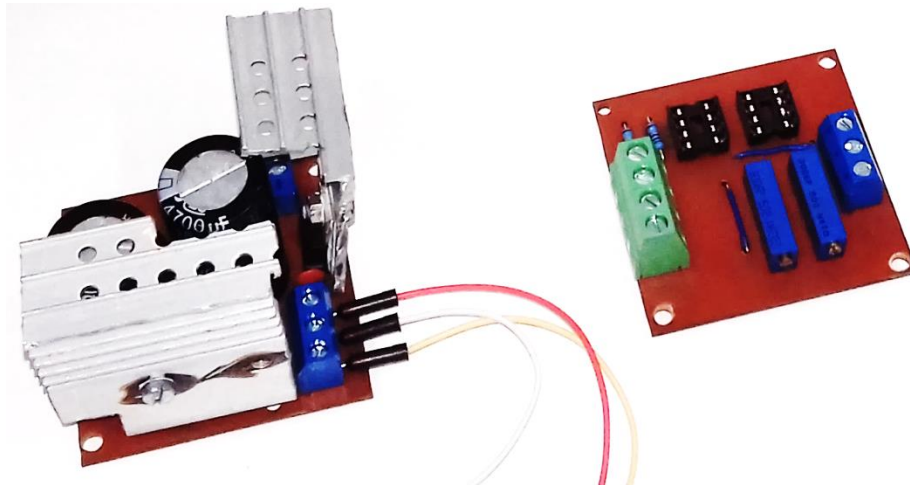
Circuitos implementados en PCB. (a) Fuente simétrica, (b) Etapa de acondicionamiento.
